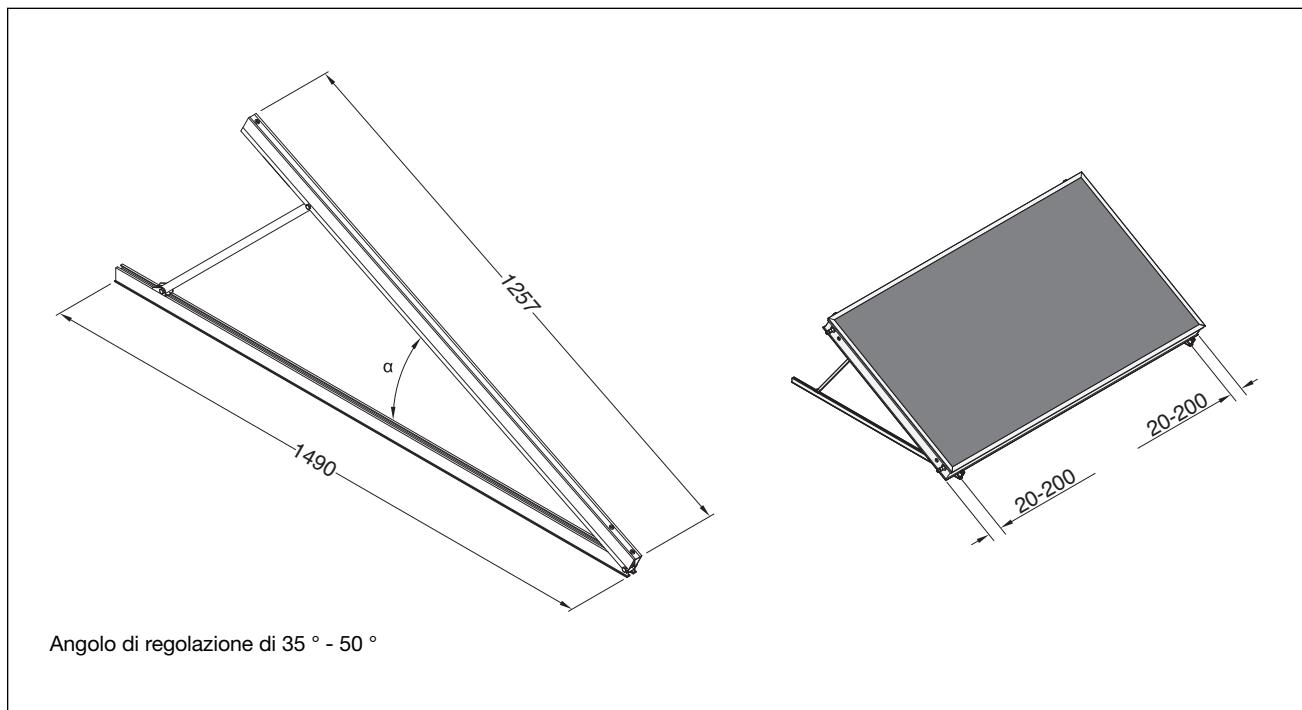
Regolazione inclinazione installazione orizzontale
